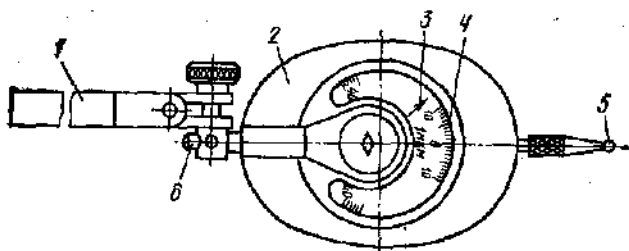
Миникатор — рычажно-пружинная головка бокового действия:
